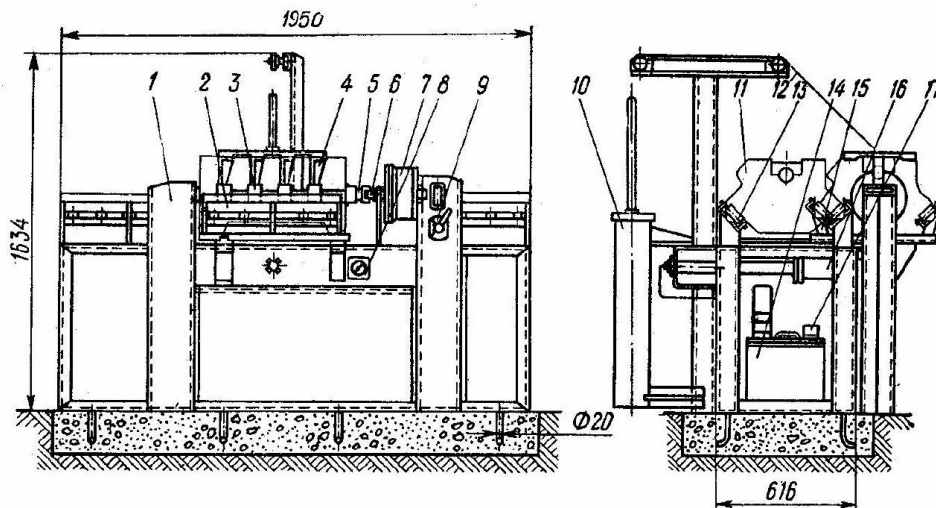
Стенд для перепрессовки втулок распределительного вала двигателя
